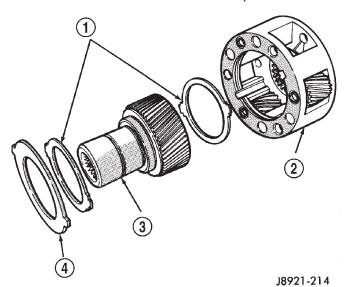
Conjunto de engranajes impulsor y de escala de baja
